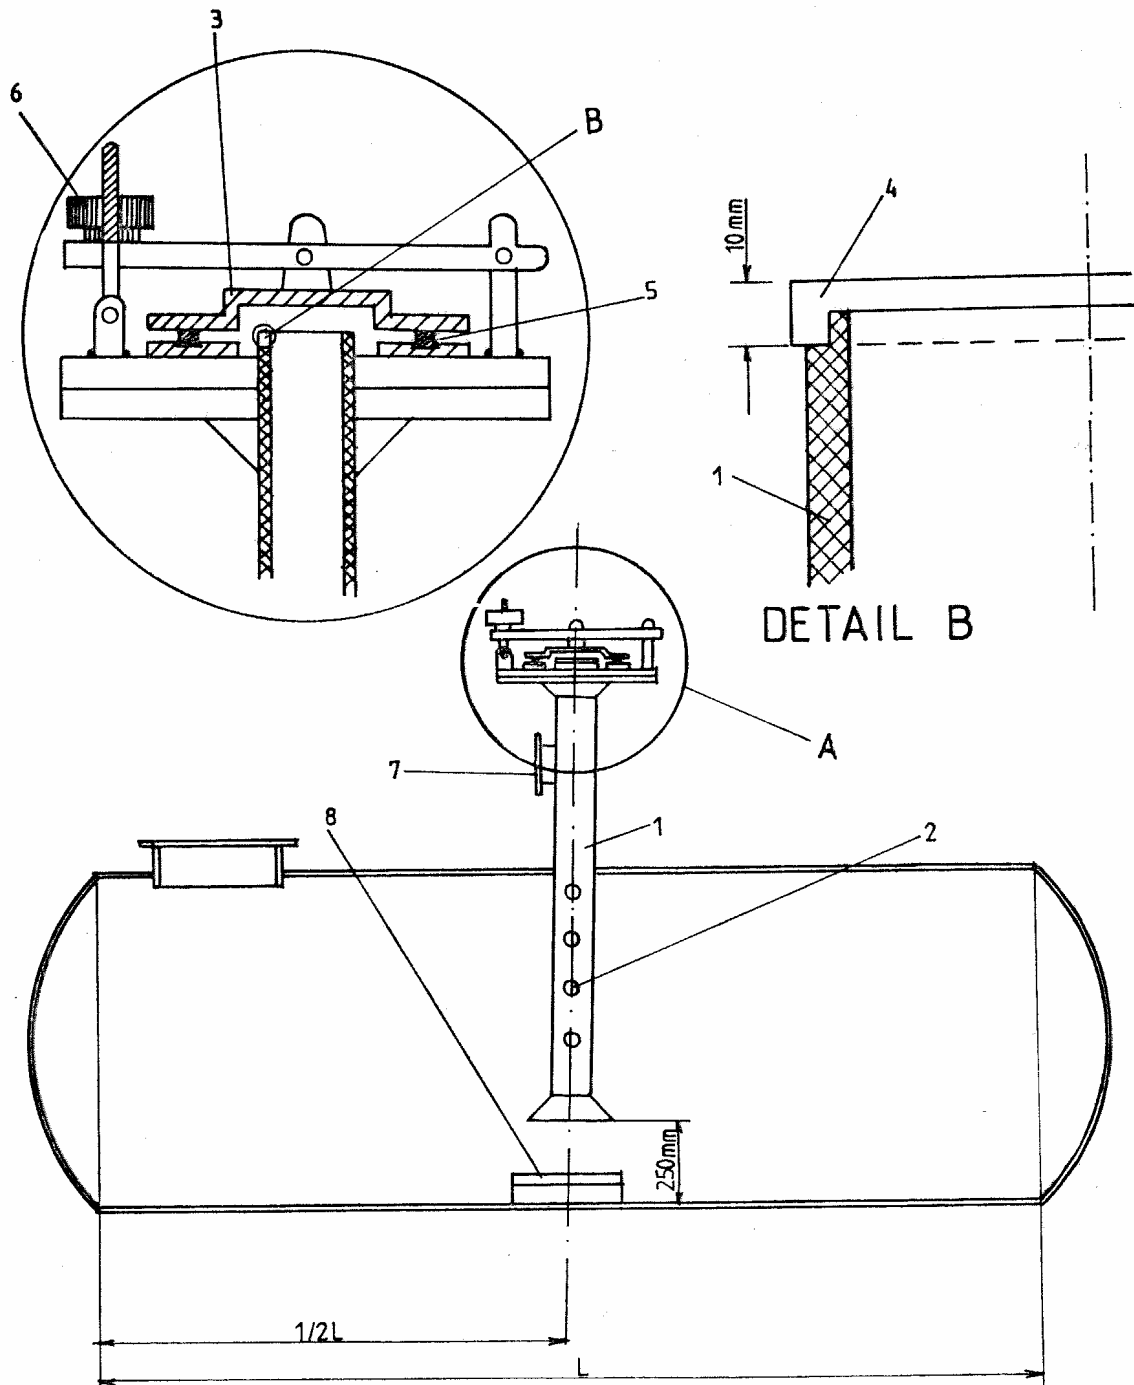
Principe de montage d'un tube de guidage sur un réservoir cylindrique horizontal
